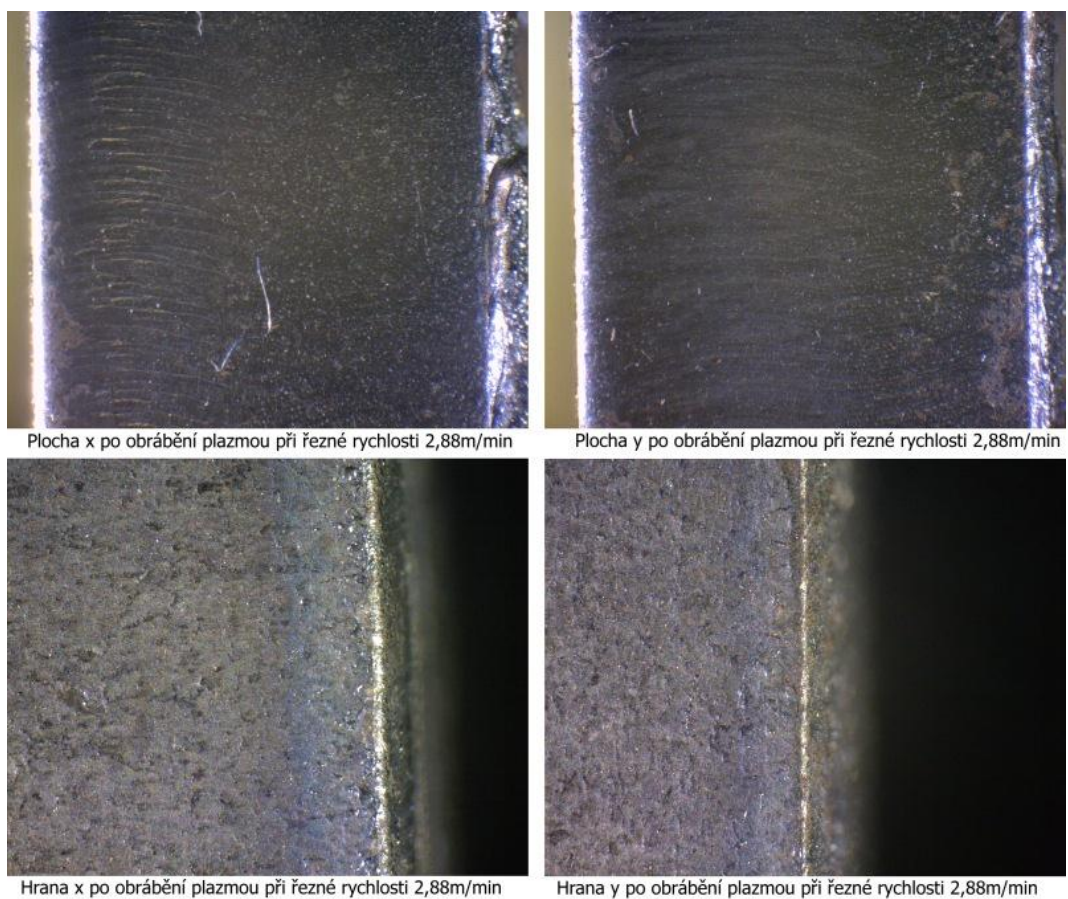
Snímky z mikroskopu vzorku 2 obráběného plazmou - materiál 11 375
